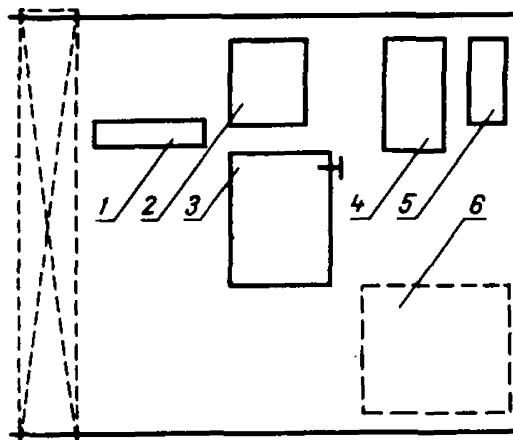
Типовая схема планировки рабочего места сборки заднего моста:
